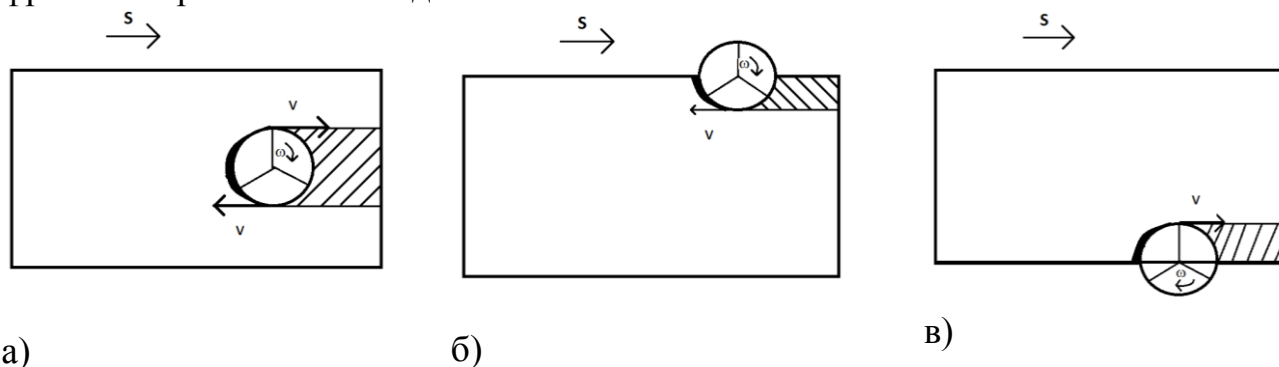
Положения торцевой фрезы относительно обрабатываемой детали
